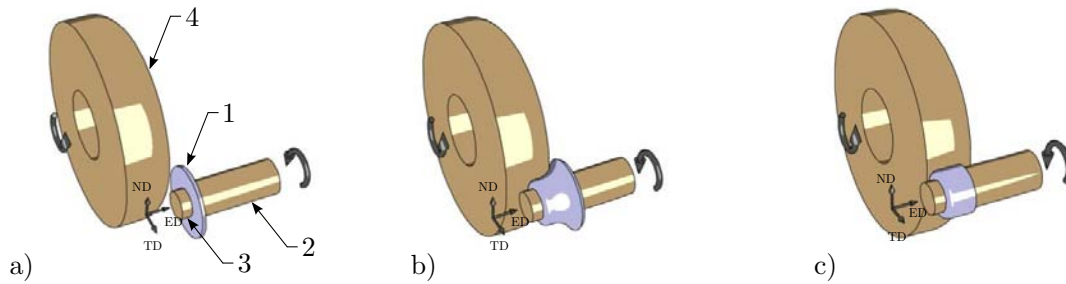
Étapes du procédé de fluotournage : a) position initiale, b) écoulement du matériau sur le mandrin et c) formation de la coupelle.
